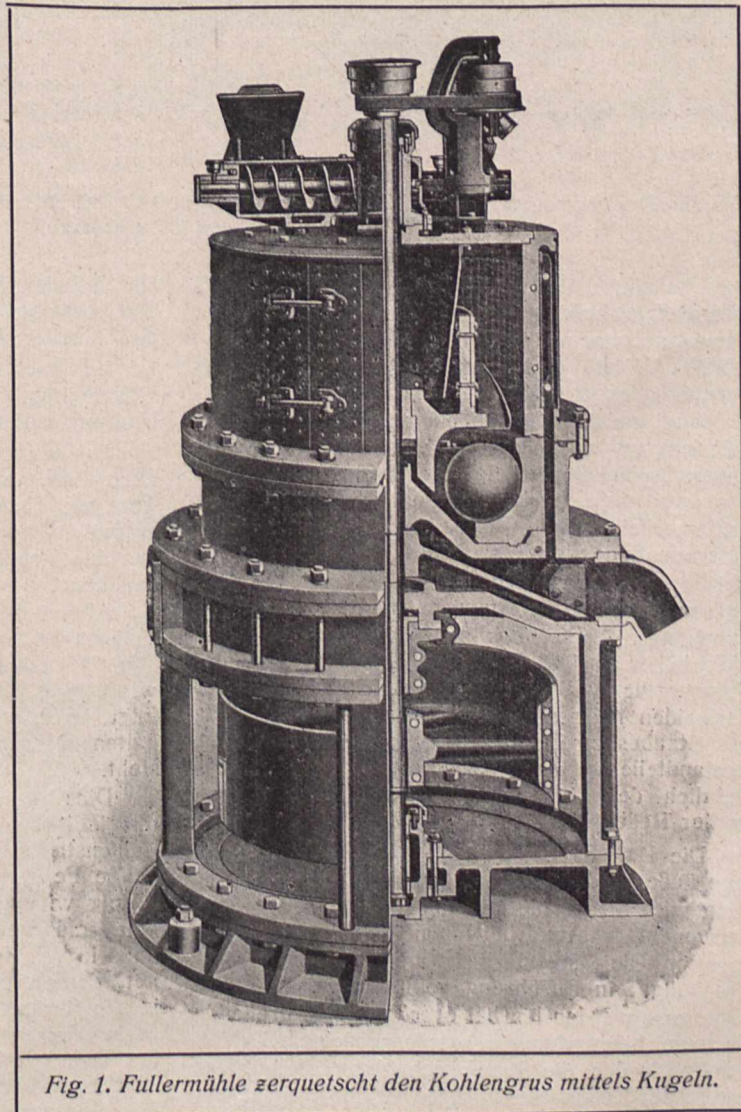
Fullermühle zerquetscht den Kohlengrus mittels Kugeln.
